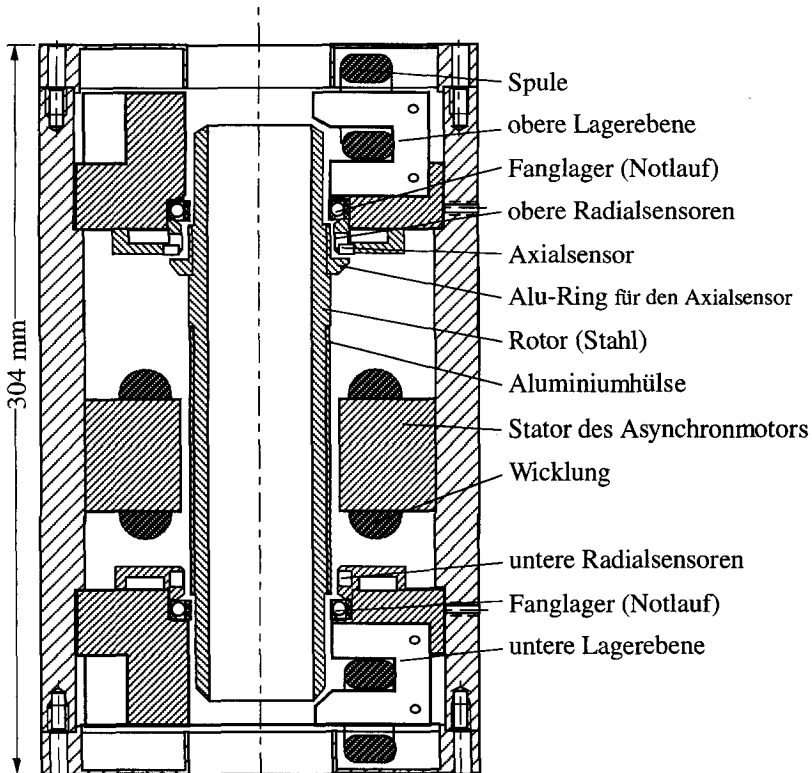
Schnitt durch die magnetgelagerte Spindel
